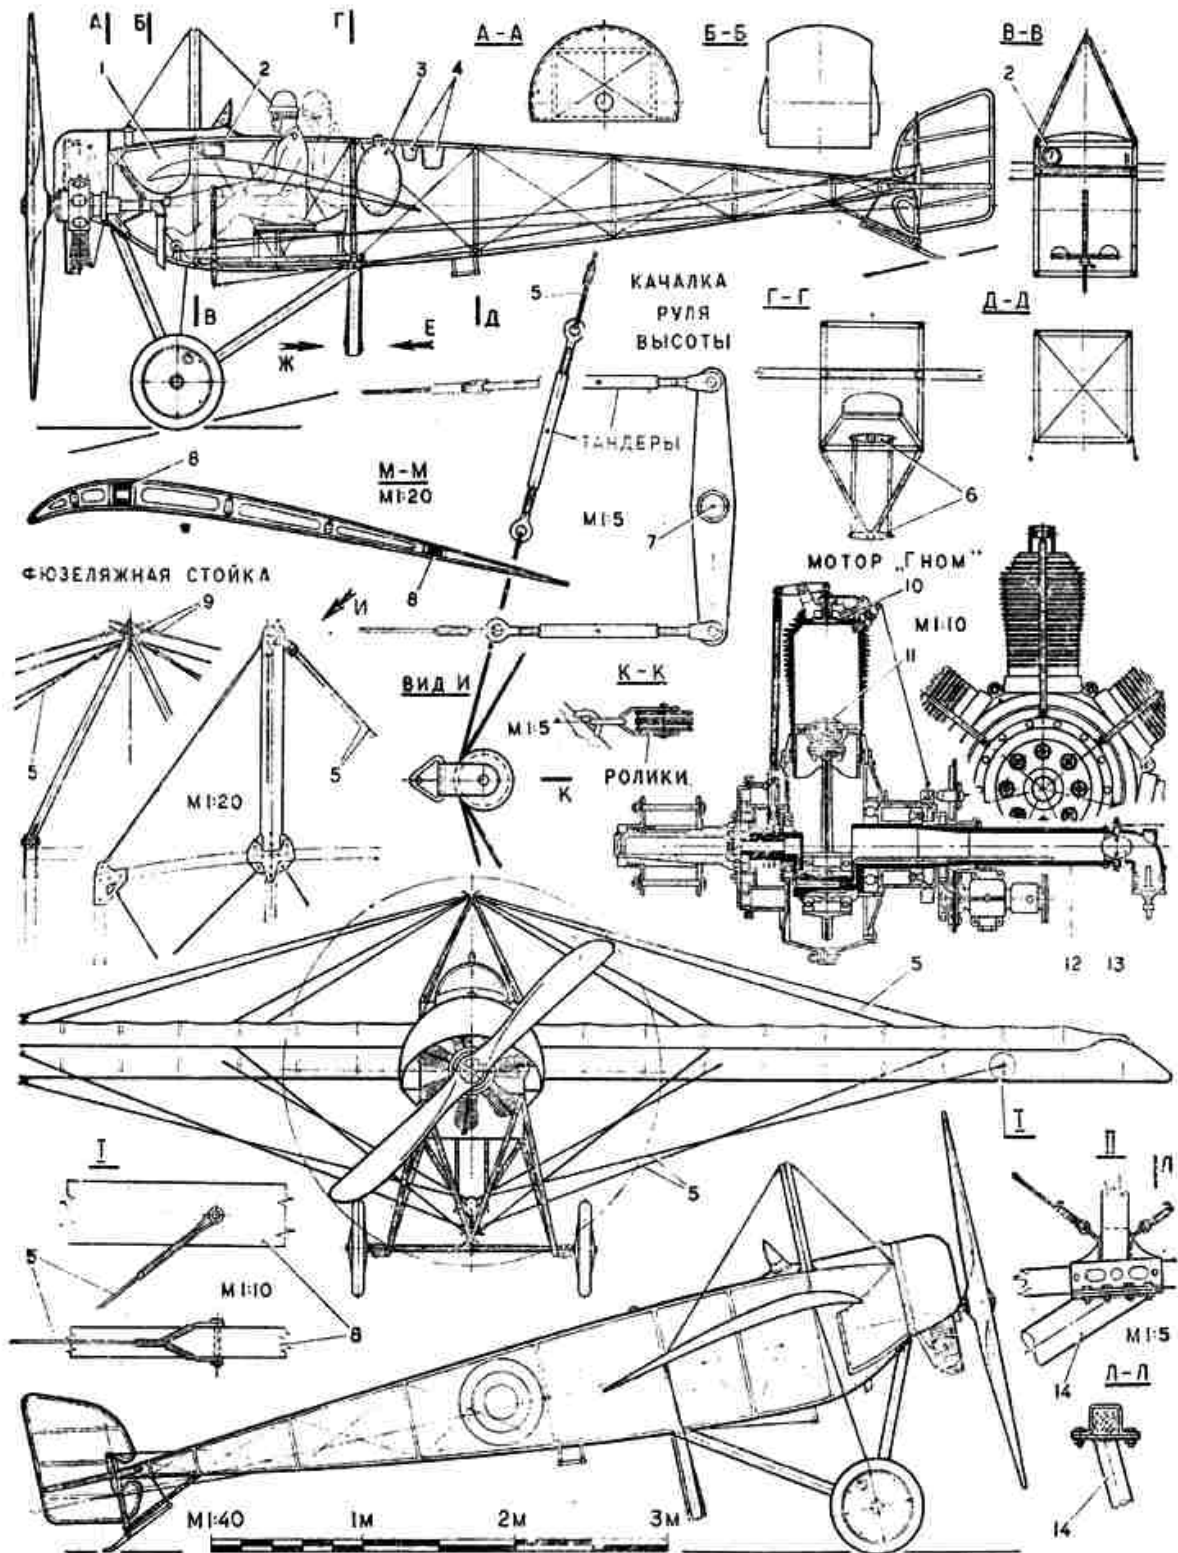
Planta da aeronave Morane-Saulnier tipo G.
